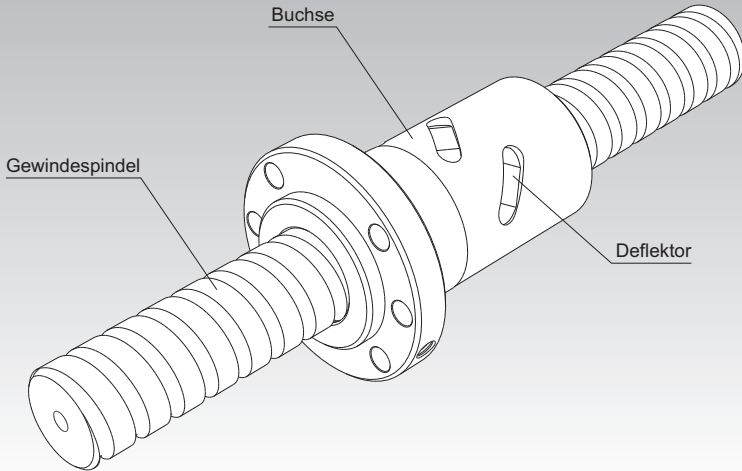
DIN-Kugelgewindetrieb (entspricht DIN 69051)
